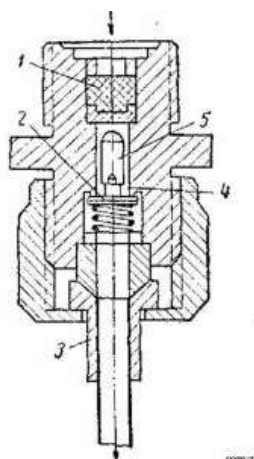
Дозирующий клапан для централизованной жидкой смазки.
